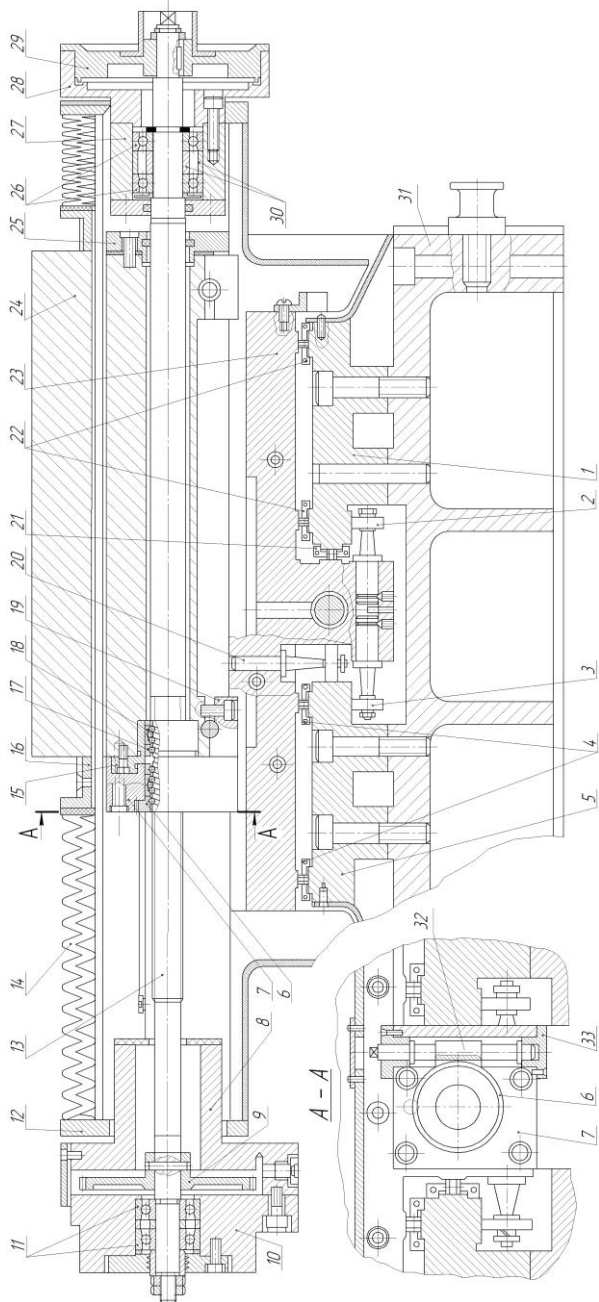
Двухкоординатный суппорт (ось X) станка мод. ТПК-125В
